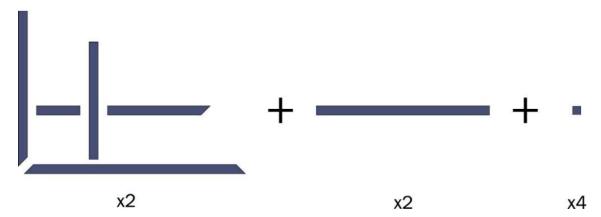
Croquis proceso de corte perfiles conjunto estático
